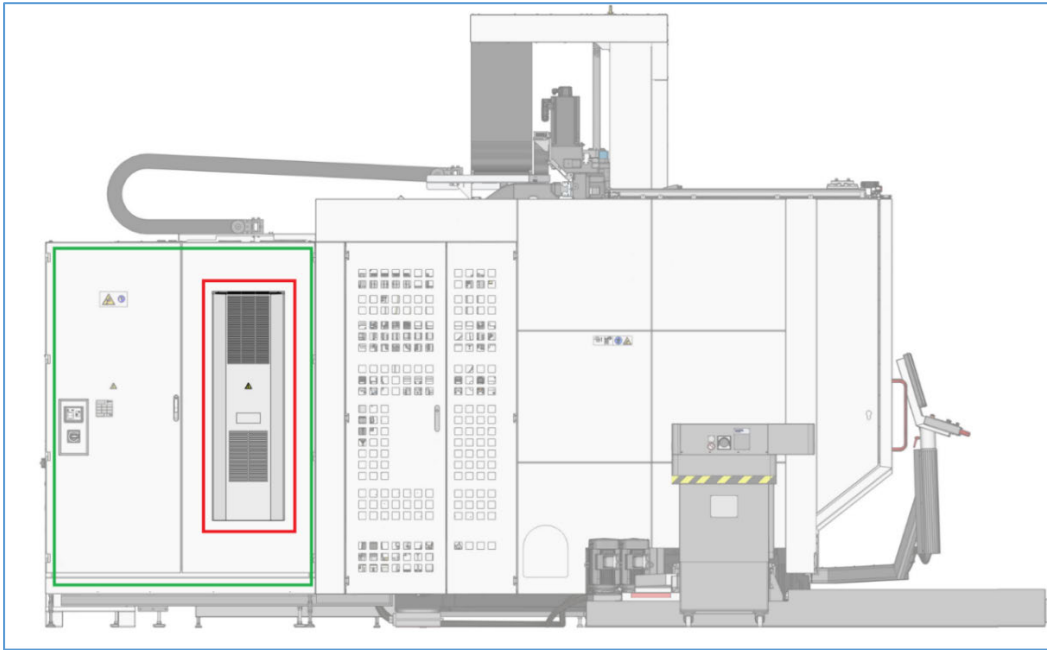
CNC-Werkzeugmaschine mit Schaltschrank (grün) und einem Klimagerät (rot) im Türanbau.
